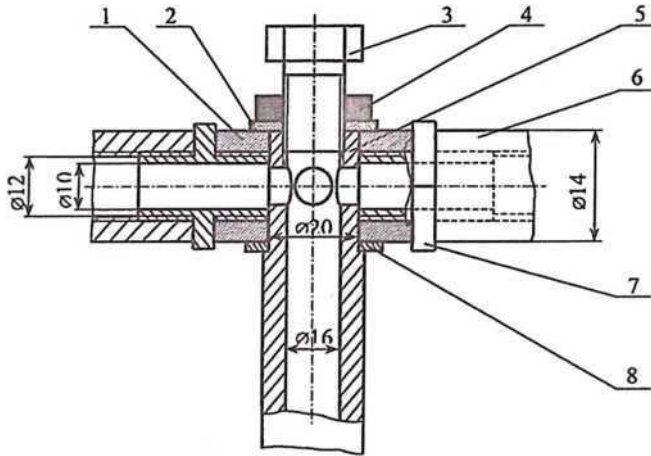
Обертова опора розбризувача: 1 — маточина; 2,8 - шайби; 3 - гвійгт; 4 - контргайка; 5 - осьовий спрямовувач обертової опори; 6 - змішні штанги; 7 — штуцер.
